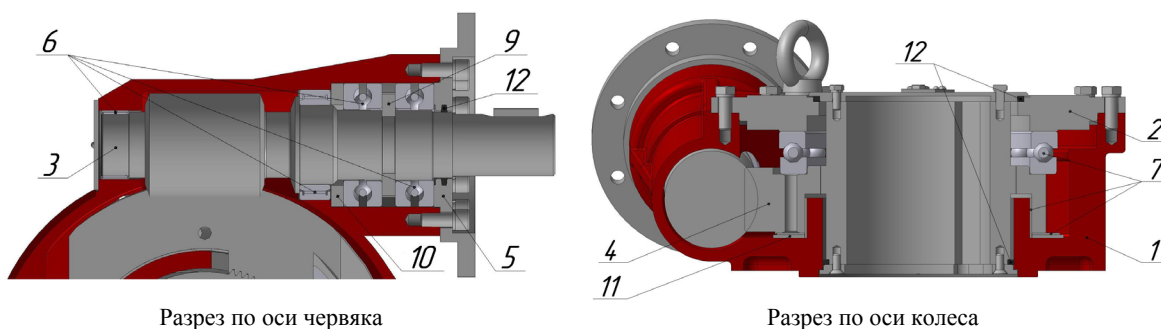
Конструкция четвертьоборотного неортогонального червячного редуктора
